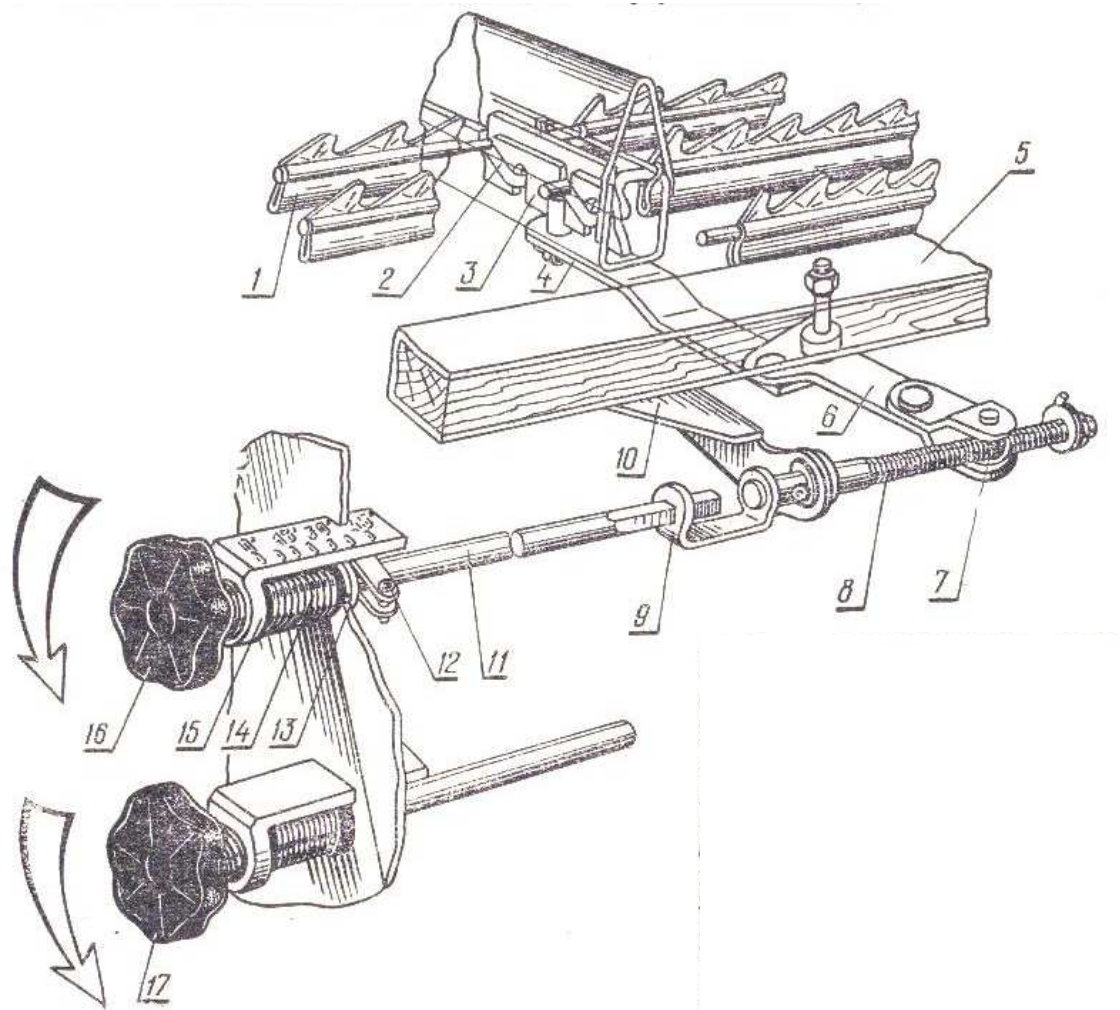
Механизм регулирования жалюзи решетки очистки комбайна СК-6: 1 – сегмент жалюзи; 2 – коленчатый валик; 3 – рейка; 4 – тяга; 5 – рамка решета; 6 – коленчатый рычаг; 7 – шарнирная гайка; 8 – винт; 9 – скоба; 10 – кронштейн; 11 – валик; 12 – фиксирующая скоба; 13 – резиновая шайба; 14 – резьбовая втулка со шкалой; 15 – гайка; 16, 17 – маховики
